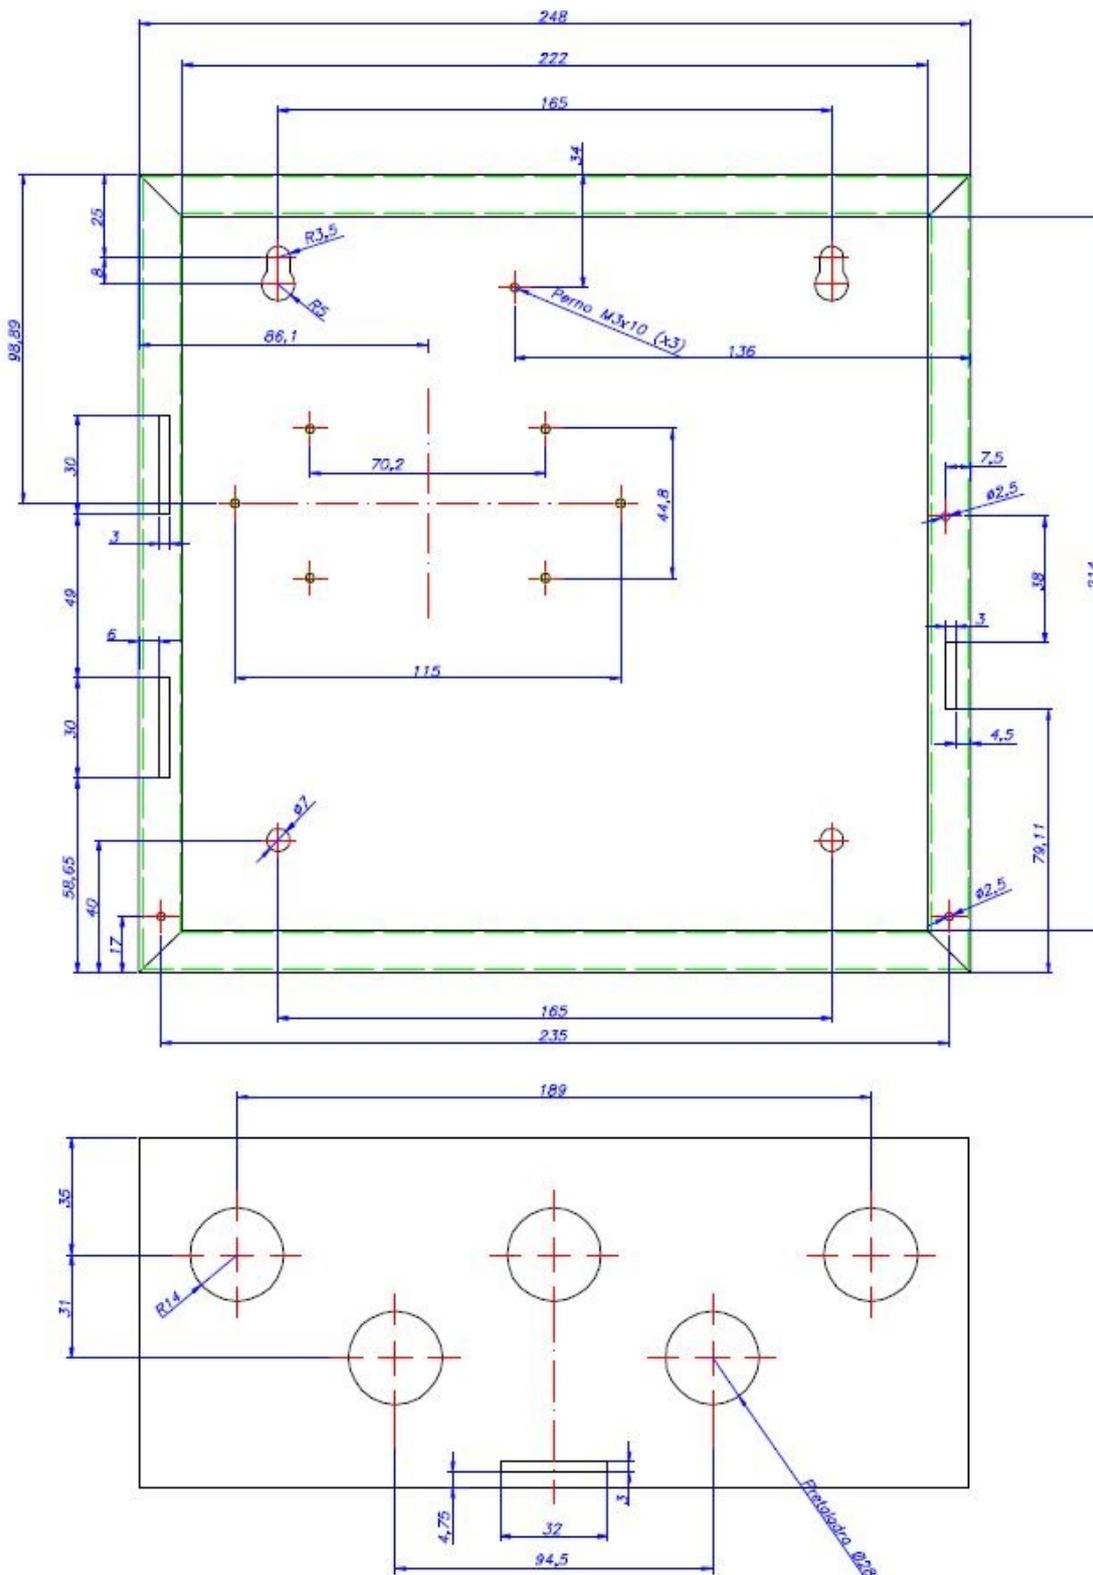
Planos da planta; furos para fixação e passagem de cabos.
